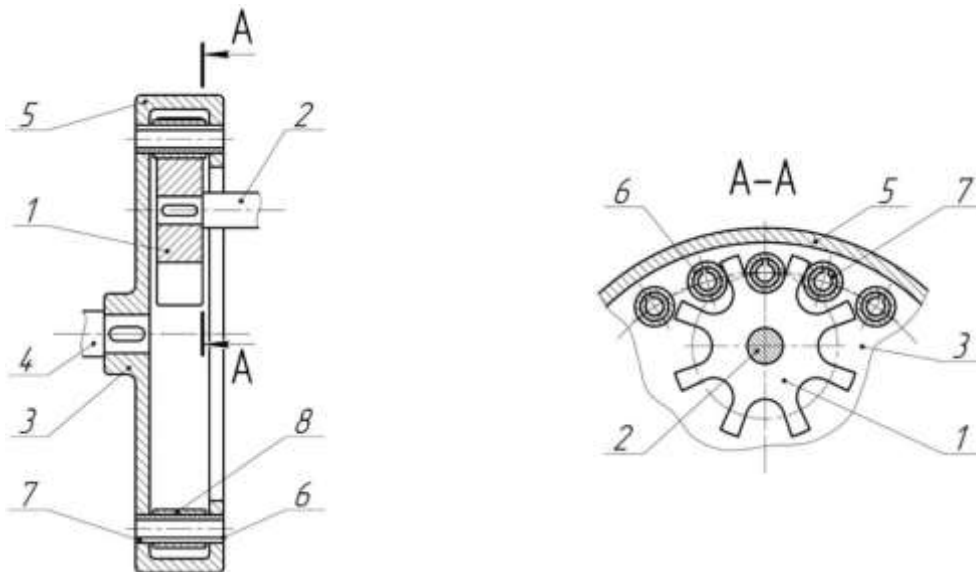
Цівкова передача (запропонована конструкція): 1 – зубчасте колесо; 2 – ведучий вал; 3 – цівкове колесо; 4 – ведений вал; 5 – обод; 6 – циліндричні отвори; 7 – цівки; 8 - ролики
